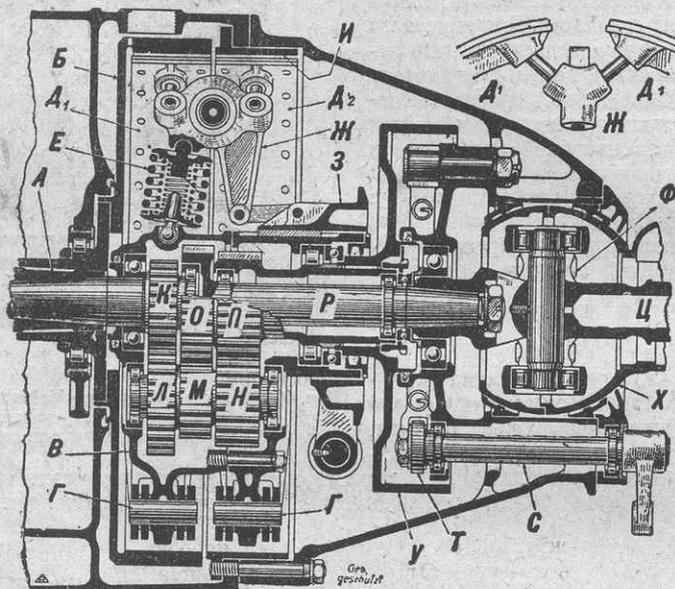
Схематический разрез планетарной коробки передач автомобиля «Майбах».
